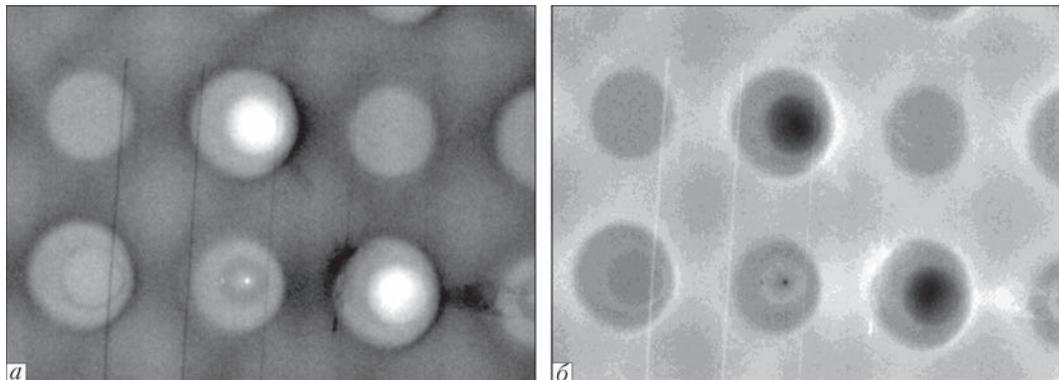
Цифровые изображения дефектного участка образца с двойной точечной сваркой, полученные с применением твердотельного преобразователя типа S10811-11: *а* – позитив; *б* – негатив
